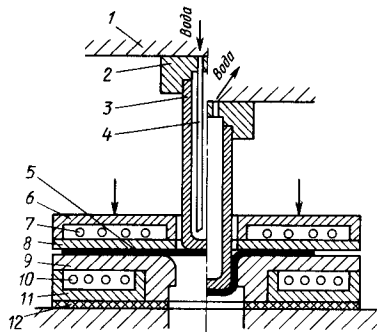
Схема штампа для вытяжки листовой заготовки с дифференцированным нагревом:
